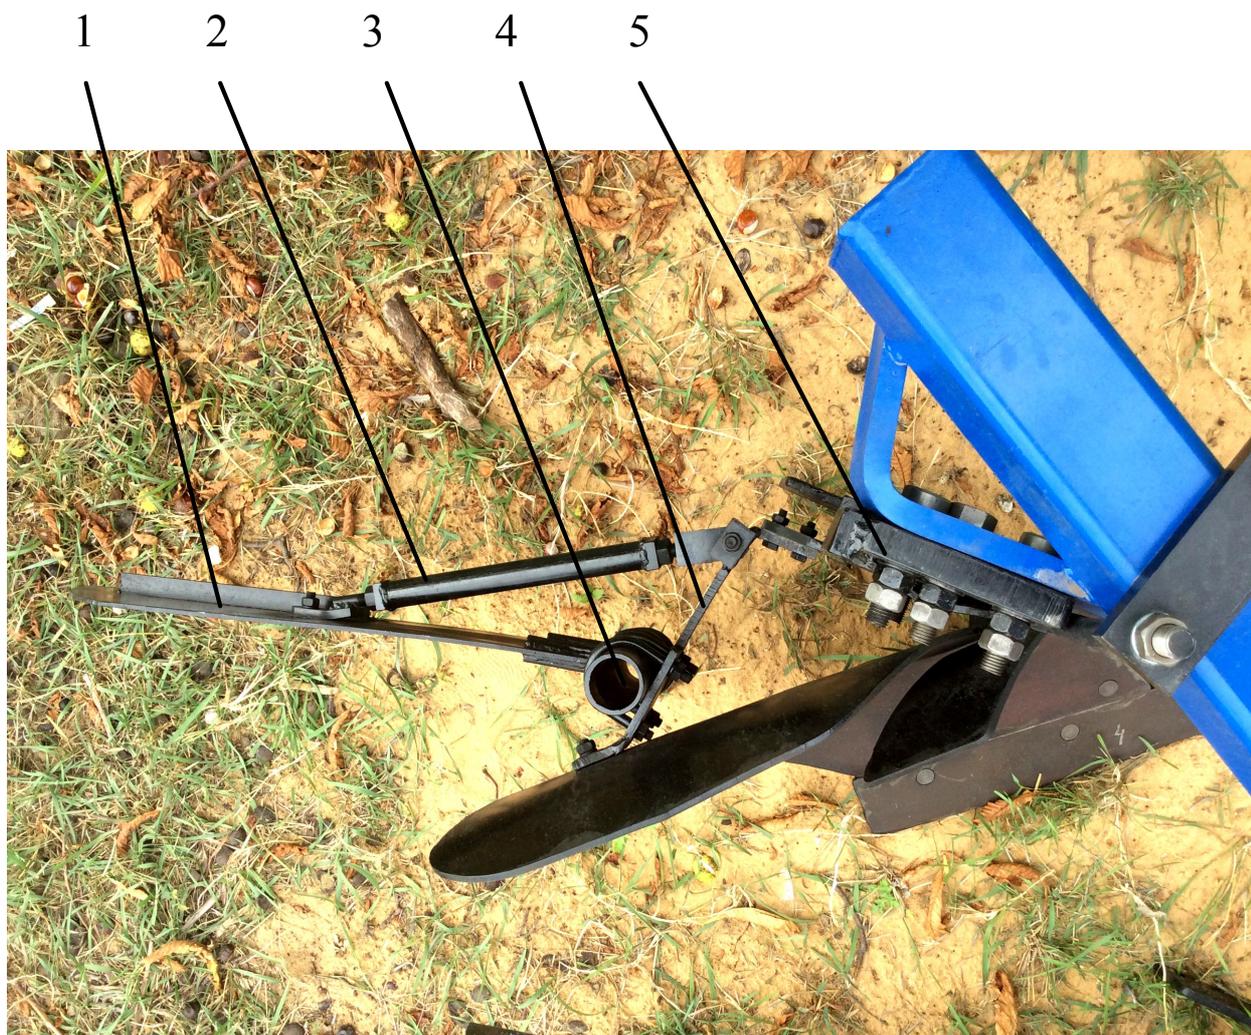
Крепление щитка к рабочему корпусу плуга (вид сверху)
